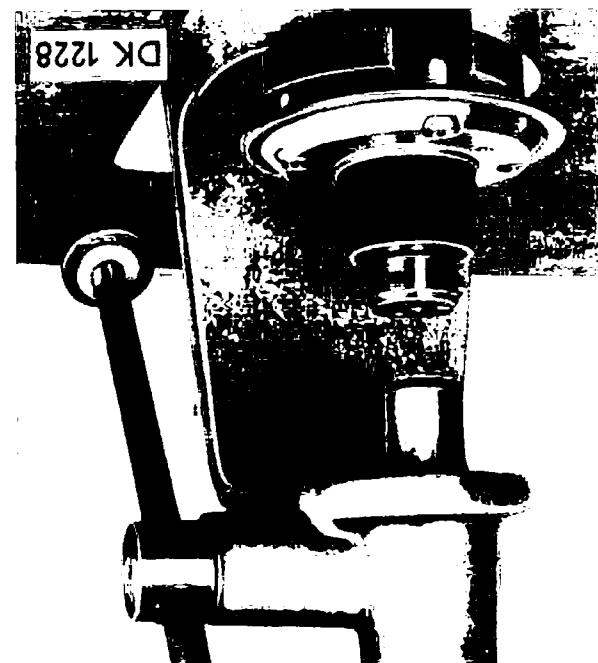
/3a Herauspressen des äusseren (kleineren) Lager rings mit dem Montage dorn MP 6-129
